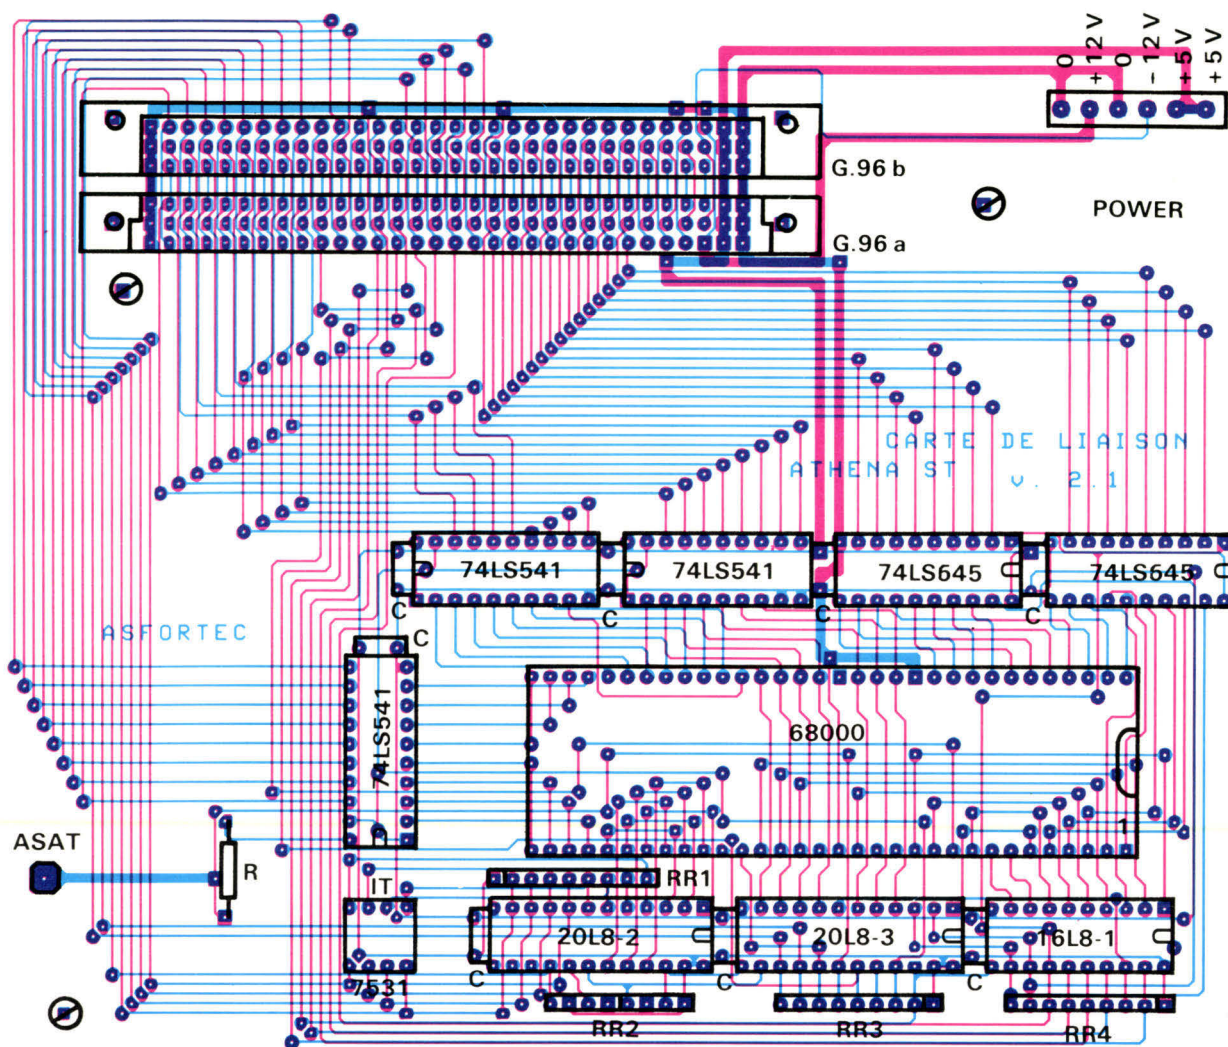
Circuit imprimé : vu côté composants et vu côté soudures. Implantation des composants.
